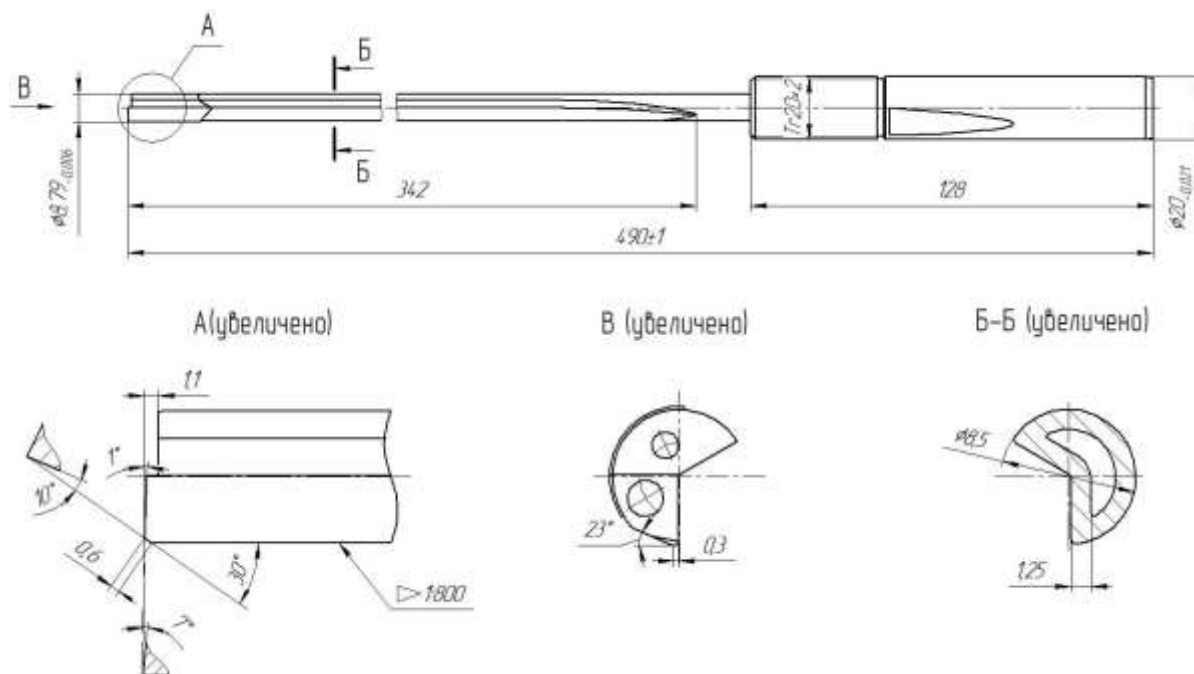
Конструктивные и геометрические параметры ружейного сверла
